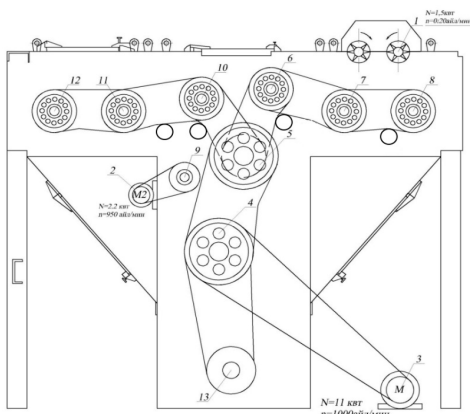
, б. Кинематическая схема бокового вида очистителя хлопка с новой компоновкой привода
